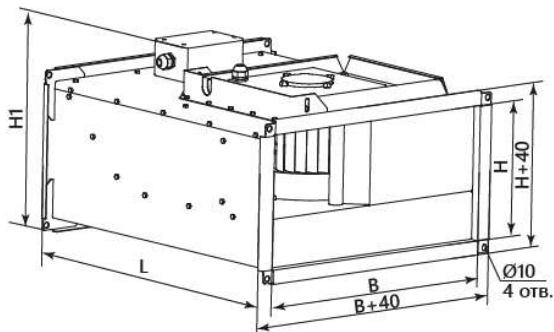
Рисунок 1 Загальний вид вентилятора типу С-РКV-V
